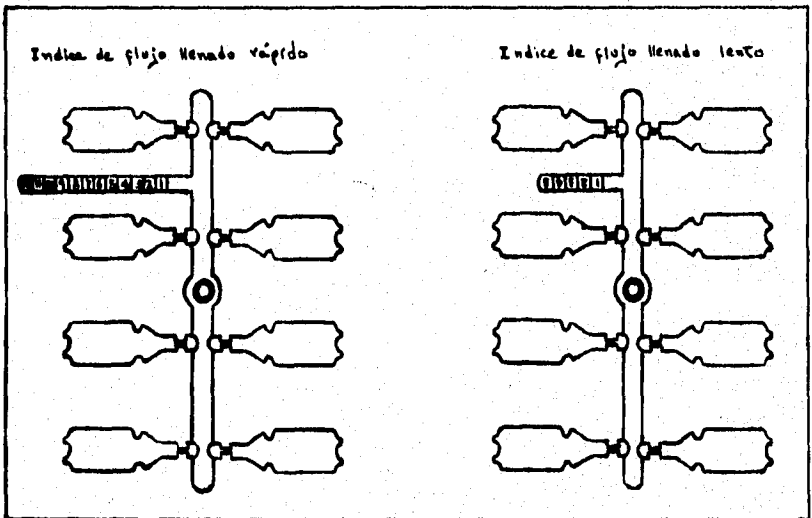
, Indicador de presión en moldes para poliolefinas.
